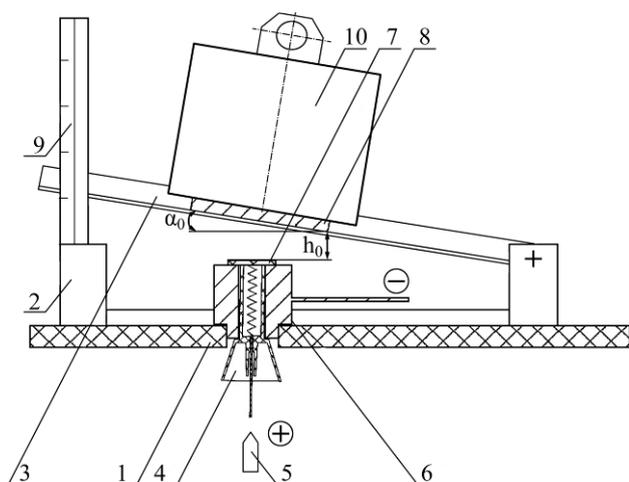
Устройство для сварки плоских образцов высокоскоростным ударом: 1 – диэлектрическая плита; 2 – рама для крепления свариваемых образцов; 3 – поворотная рама; 4 – электровзрывной патрон; 5 – высоковольтный электрод; 6 – втулка; 7 – метаемый образец; 8 – неподвижный образец; 9 – угломерная линейка; 10 – груз.
